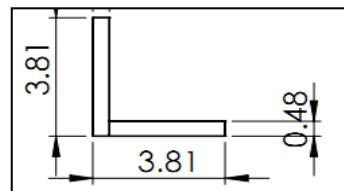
Perfil del soporte de la estructura, MBC-E-9-3.
